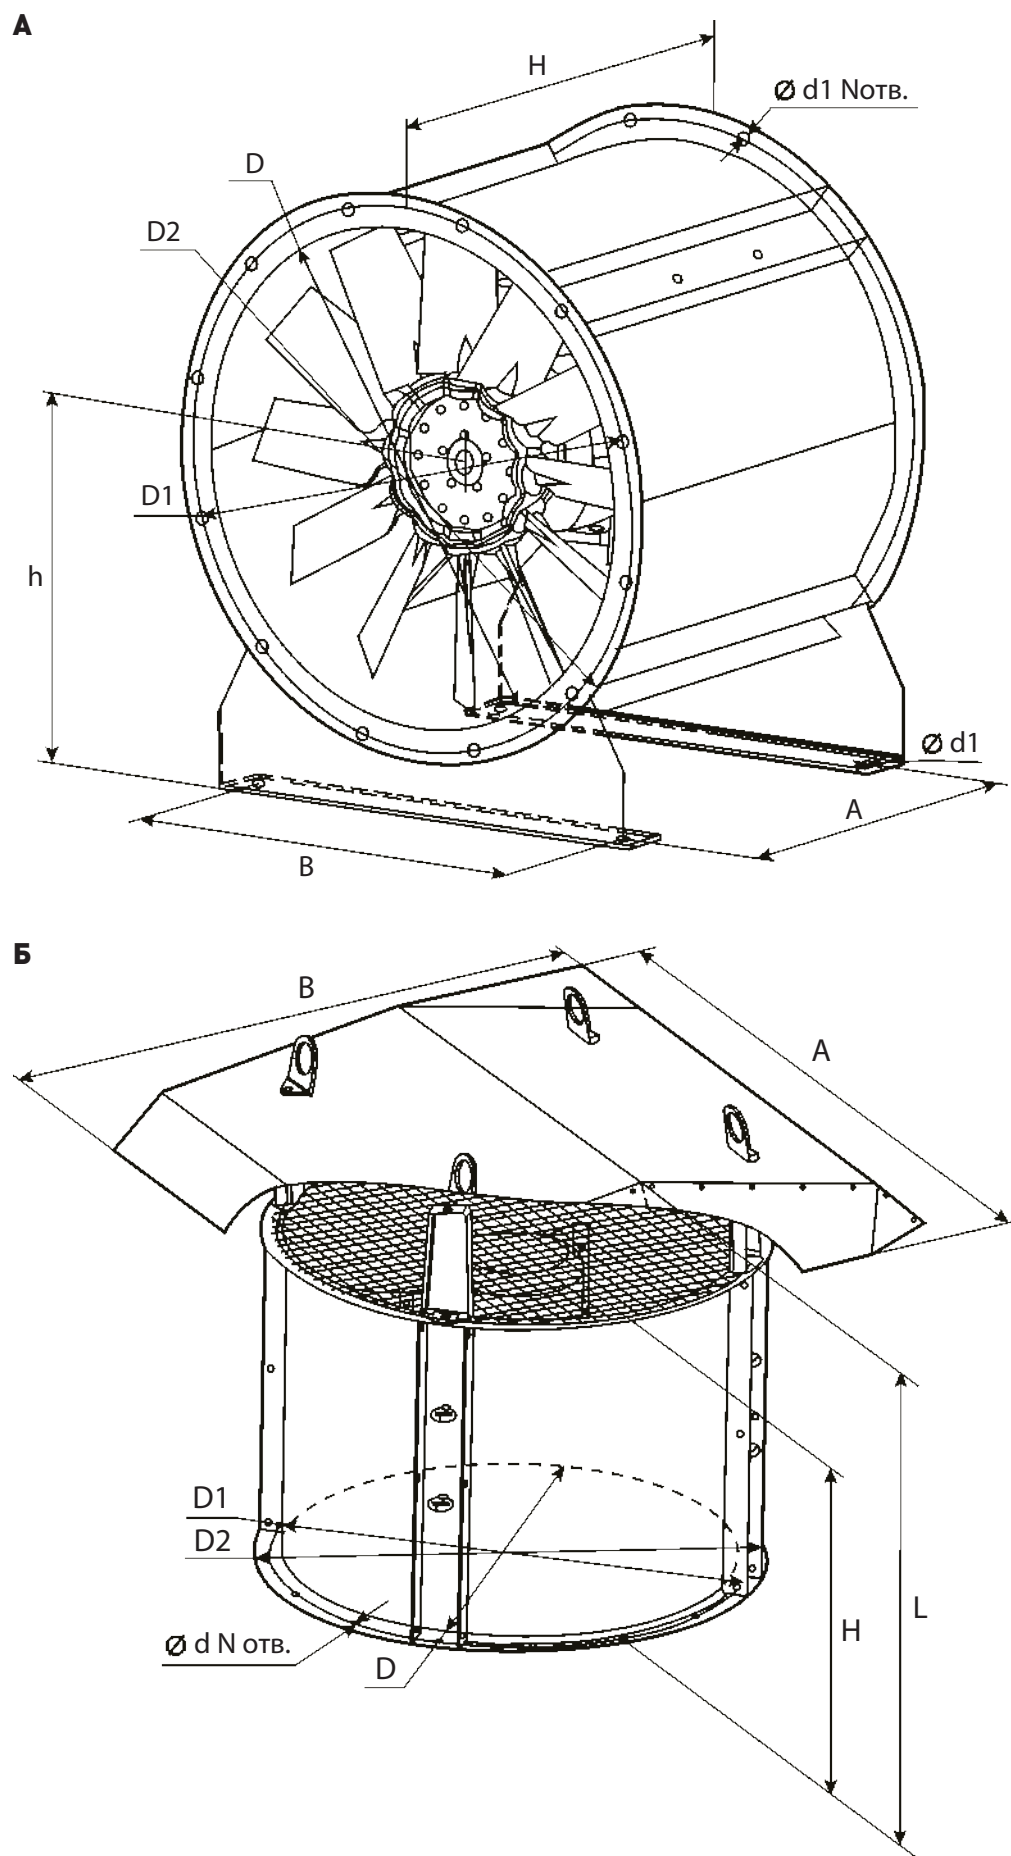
Осевой вентилятор: А – на монтажных опорах; Б – с крышей
